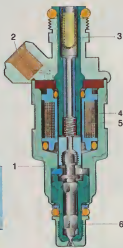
Форсунка: 1 — корпус; 2 — электрический разъем; 3 — фильтр; 4 — обмотка соленоида; 5 — пружина; 6 — распылитель.
